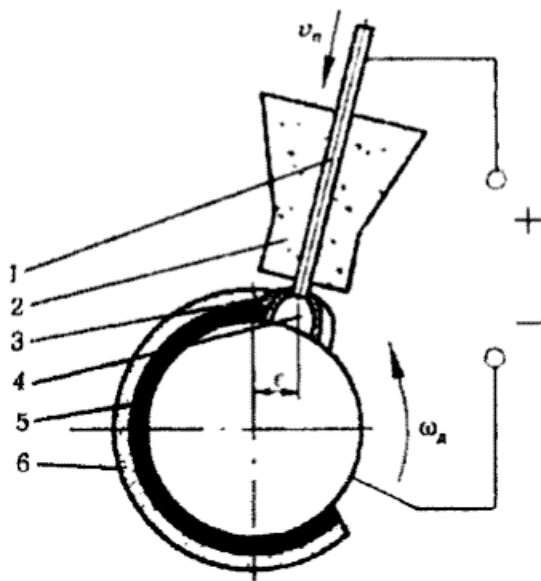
Схема наплавлення під шаром флюсу: 1 – електрод; 2 – бункер з флюсом; 3 – оболонка розплавленого флюсу; 4 – газова бульбашка; 5 – наплавлений метал; 6 – шлакова кірка; e – зміщення електрода з zenіту; v_n – швидкість подачі дроту; ω_d – кутова частота обертання деталі
